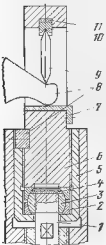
Соединение штока клапана и деталей распределительного устройства
